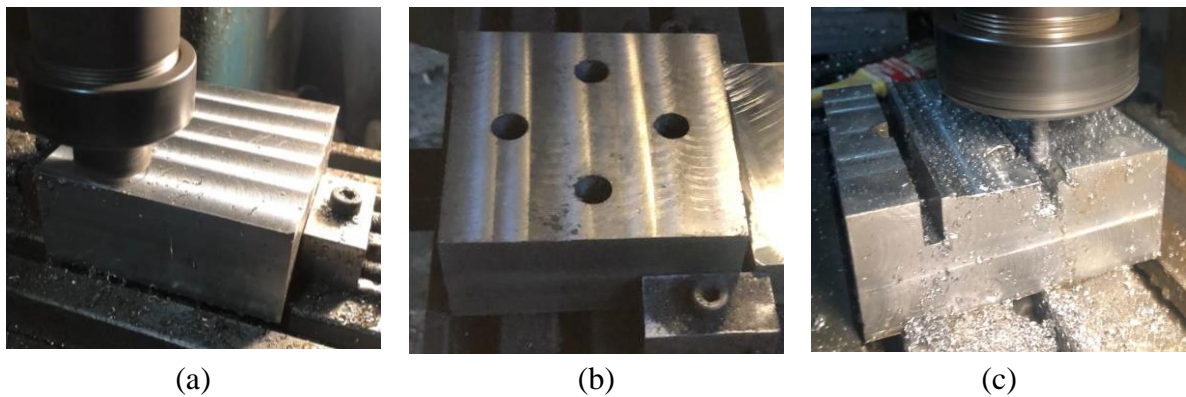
Etapas da usinagem do dispositivo: (a) esquadrejamento e altura; (b) furos para a fixação no dinamômetro; (c) desbaste da cavidade de fixação.
